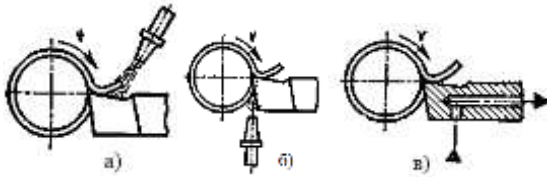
Схеми змащування під час різання: а – з верхнім підводом рідини; б – з нижнім; в – охолодження інструмента
